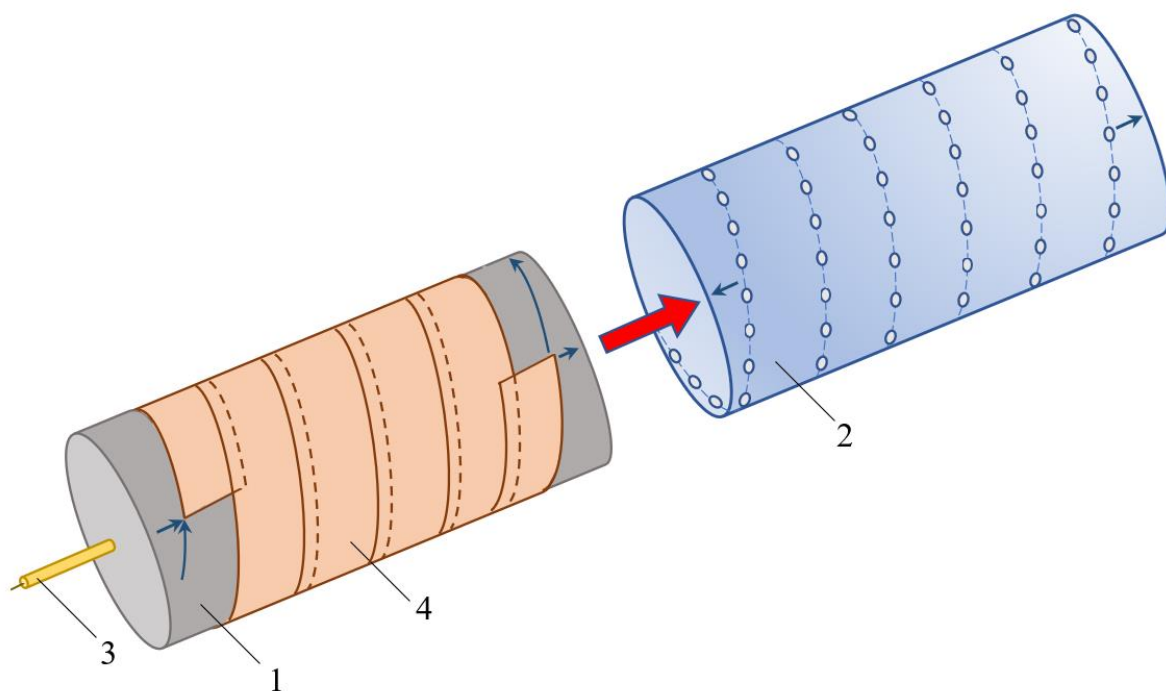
Пристрій для створення заготовки ковбасної оболонки:
